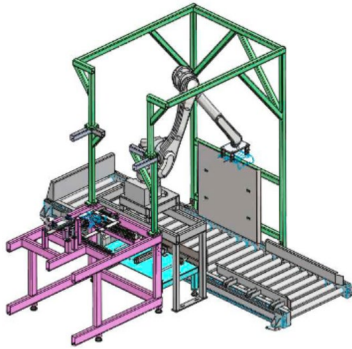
Posto de inspeção e embalagem automática de suspension mat [30]
